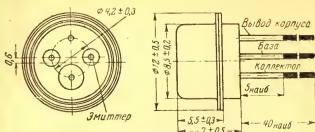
Габаритный чертеж транзисторов П504—П505А.
